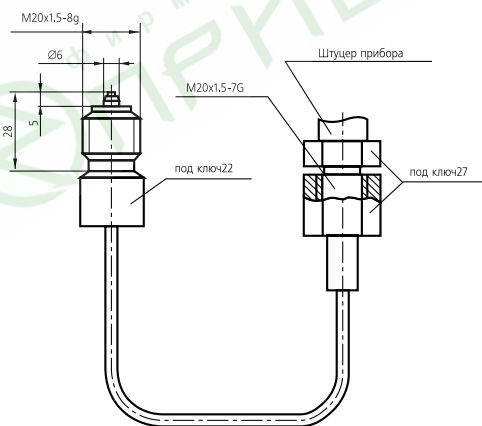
Рукав соединительный гибкий. Габаритные и присоединительные размеры
